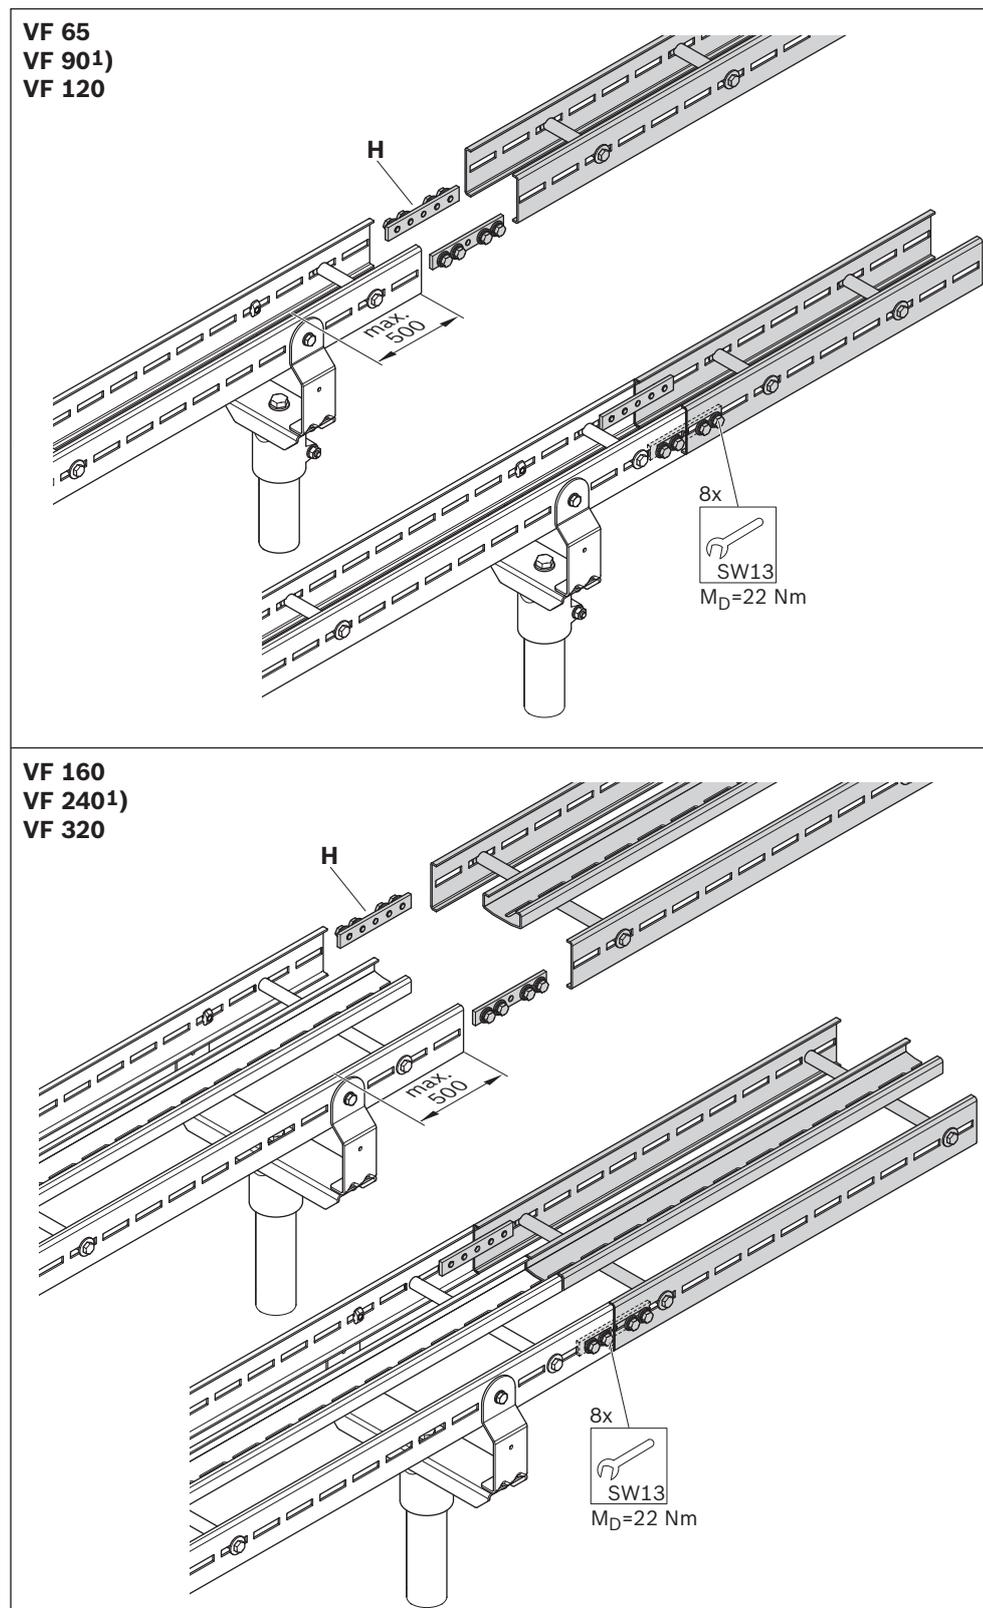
System STS, Strecke auf Streckenstützen montieren
